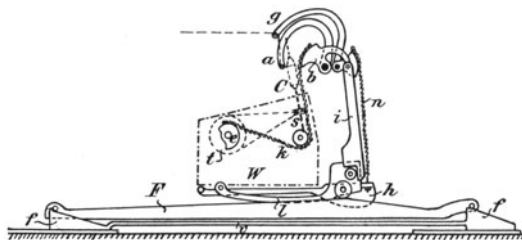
Die Windungswerkzeuge des Absetzspinners.
